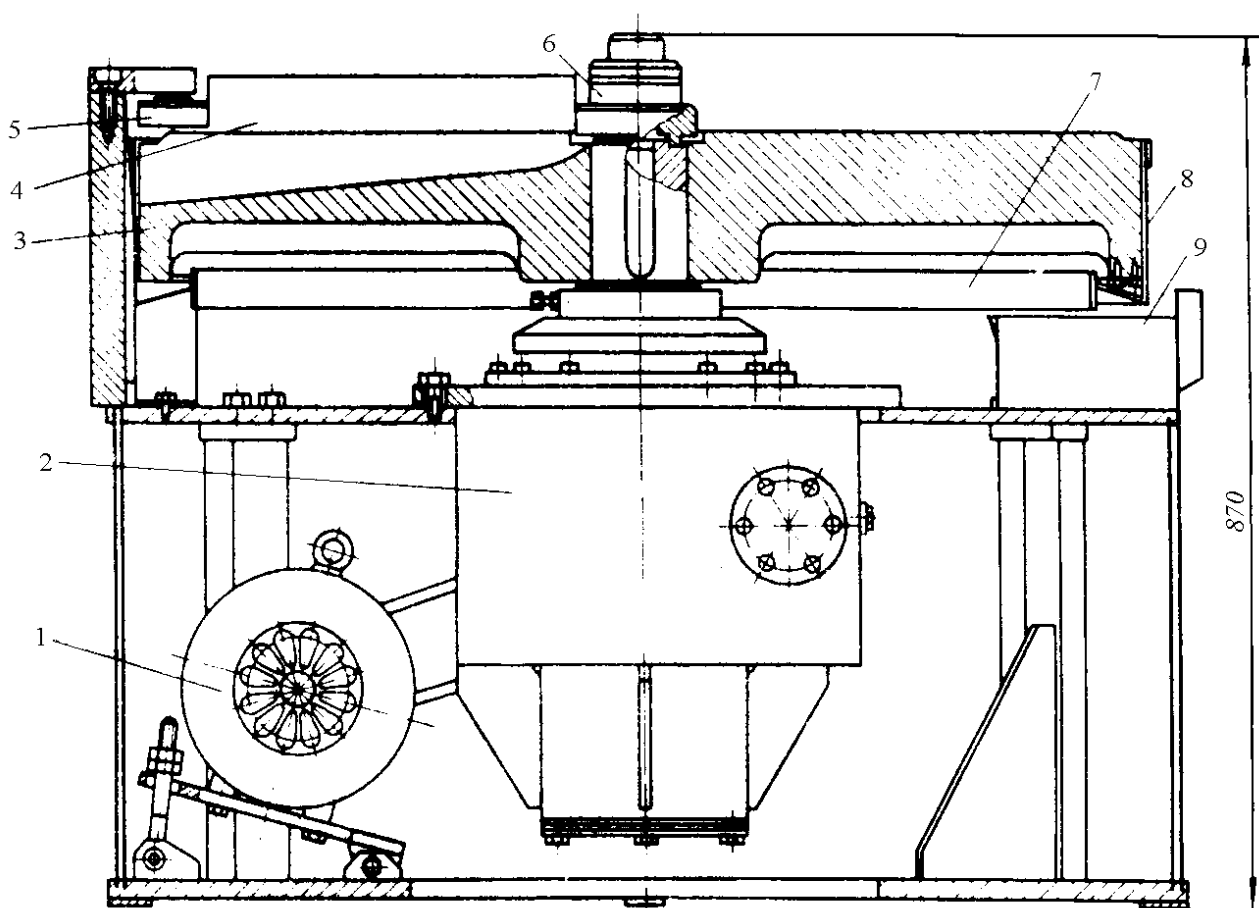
Станок для притирки клиньев клиновых задвижек.
